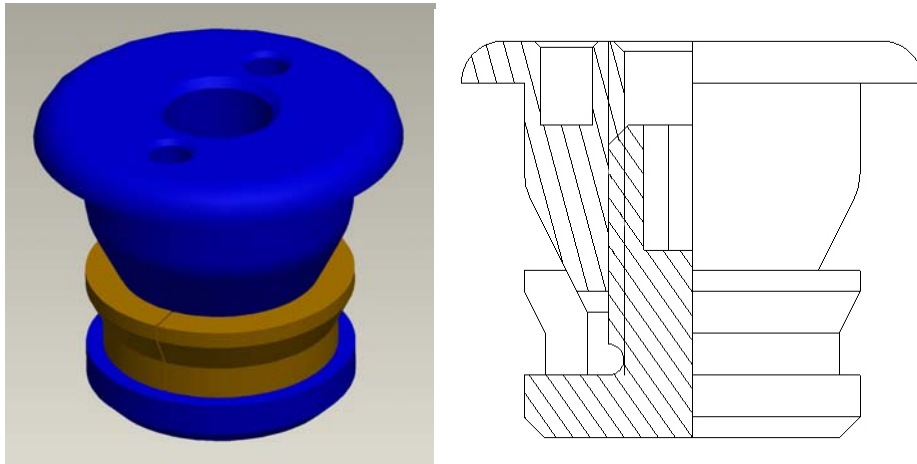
3D-Modell und Schnittzeichnung der SE-Schraube in Pro/Engineer Wildfire
